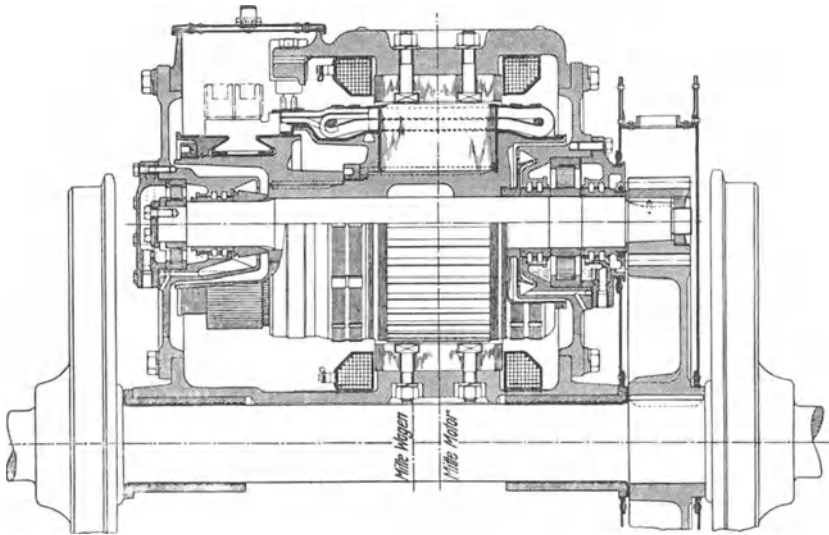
Schnitt durch einen gekapselten Motor (BBC).
